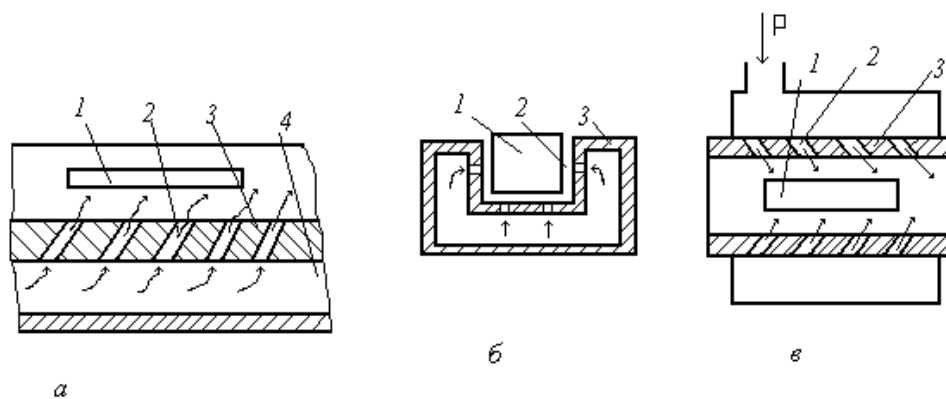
Схема пневматических транспортеров: а – открытая; б – полуоткрытая; в – закрытая с трубчатым лотком
